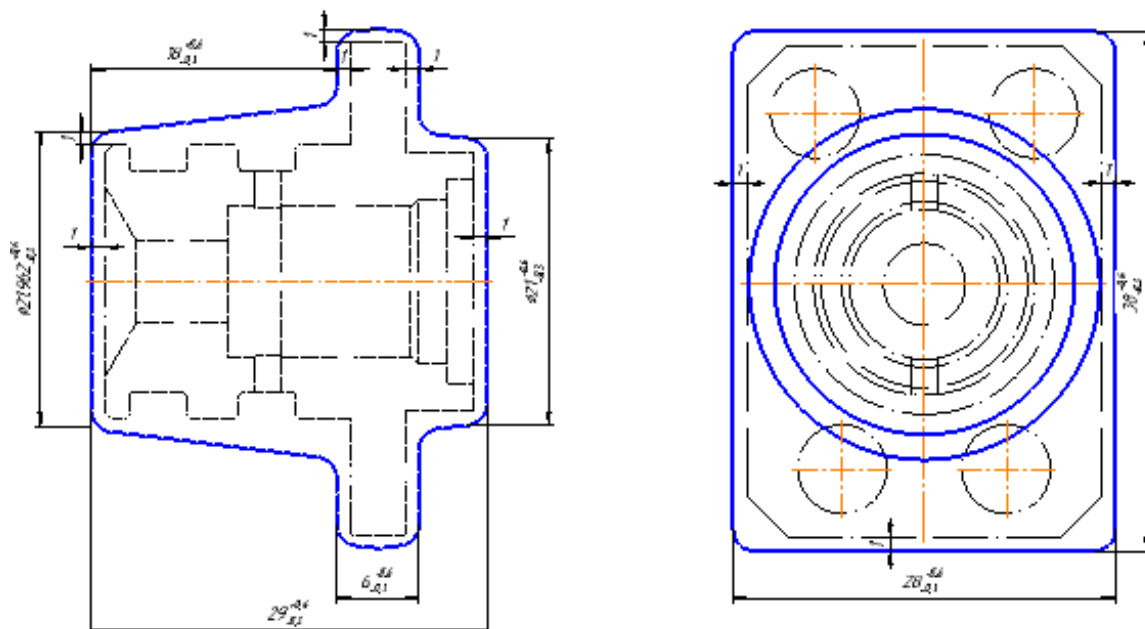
Эскиз заготовки – штамповки детали «Заглушка»
